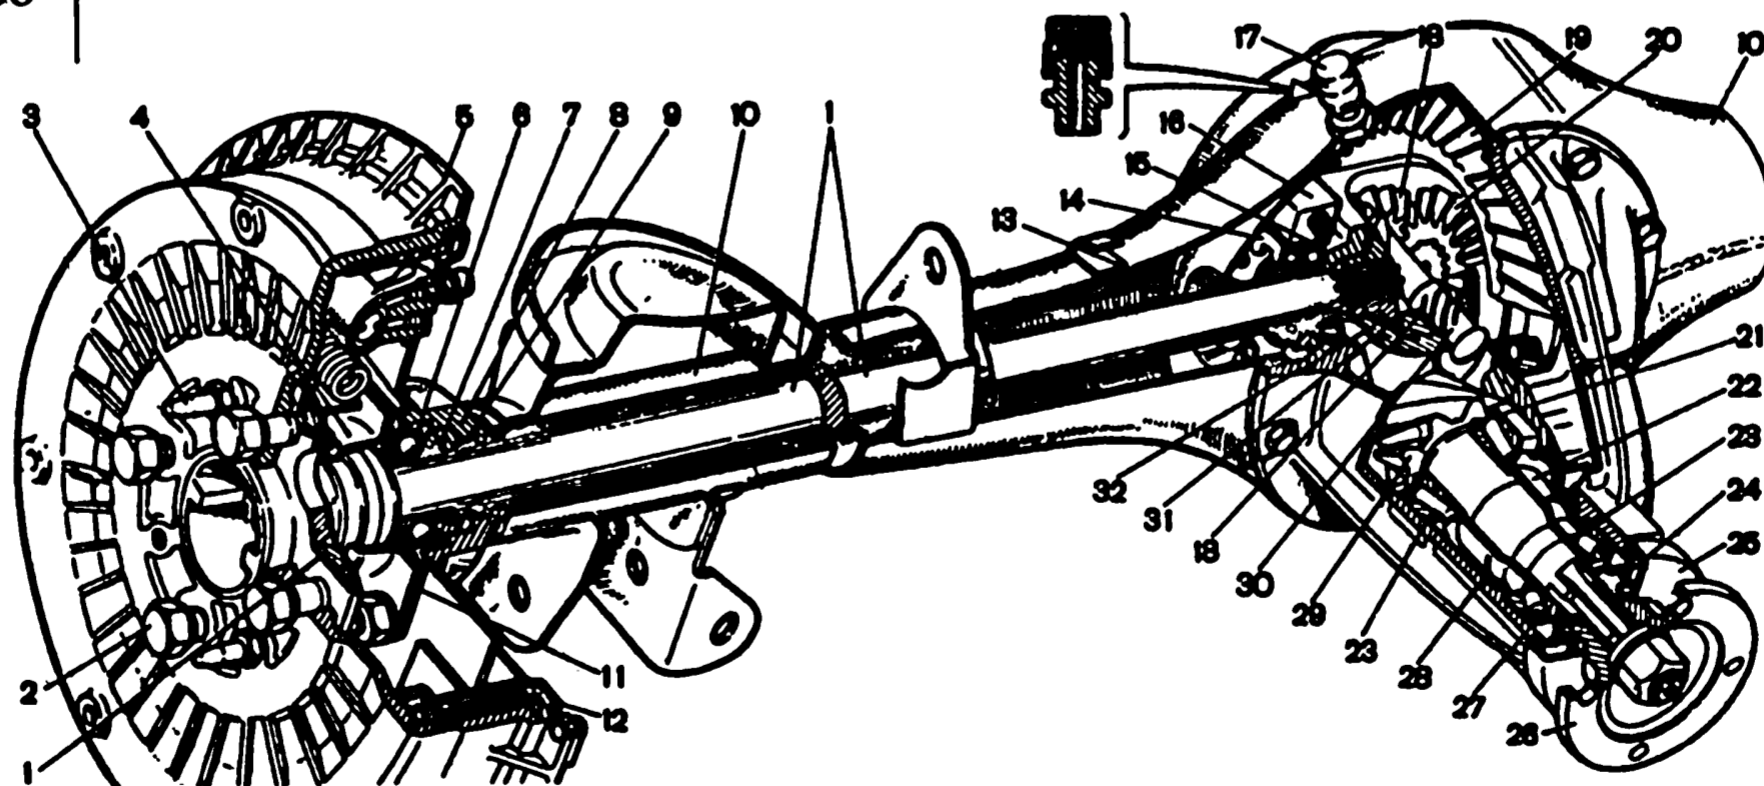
Задний мост: 1 - полуось; 2 - болт крепления колеса; 3 - направляющий штифт; 4 - маслоотражатель; 5 - тормозной барабан; 6 - подшипник полуоси; 7 - запорное кольцо; 8 - фланец балки заднего моста; 9 - сальник полуоси; 10 - балка заднего моста; 11 - пластина крепления подшипника; 12 - щит заднего тормоза; 13 - направляющая полуоси; 14 - регулировочная гайка; 15 - подшипник коробки дифференциала; 16 - крышка подшипника; 17 - сапун; 18 - сателлит; 19 - ведомая шестерня; 20 - шестерни полуосей; 21 - регулировочное кольцо ведущей шестерни; 22 - распорная втулка; 23 - подшипники ведущей шестерни; 24 - сальник ведущей шестерни; 25 - грязеотражатель; 26 - фланец; 27 - маслоотражатель; 28 - картер редуктора заднего моста; 29 - ведущая шестерня; 30 - ось сателлитов; 31 - регулировочная шайба; 32 - коробка дифференциала; 33 - болт; 34 - пластина
